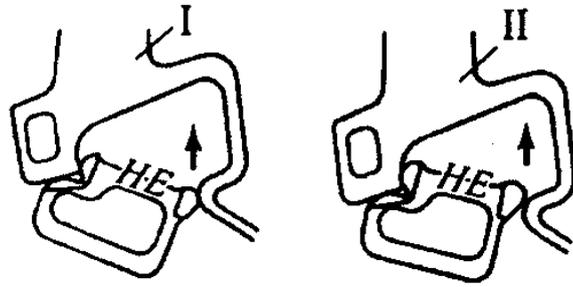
Проверка ширины зева корпуса автосцепки шаблоном 821 р-1. I – корпус годен;
